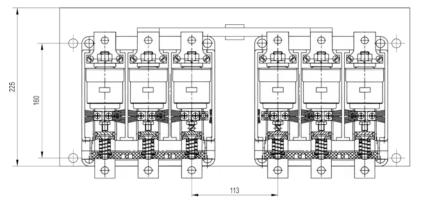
Габаритные размеры КВТ(Р)-1,14-80/125/160
